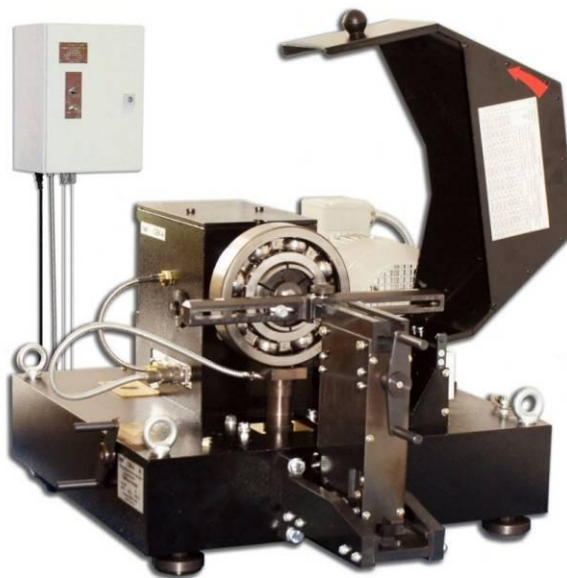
Общий вид стенда вибрационного контроля подшипников качения СВК-А
